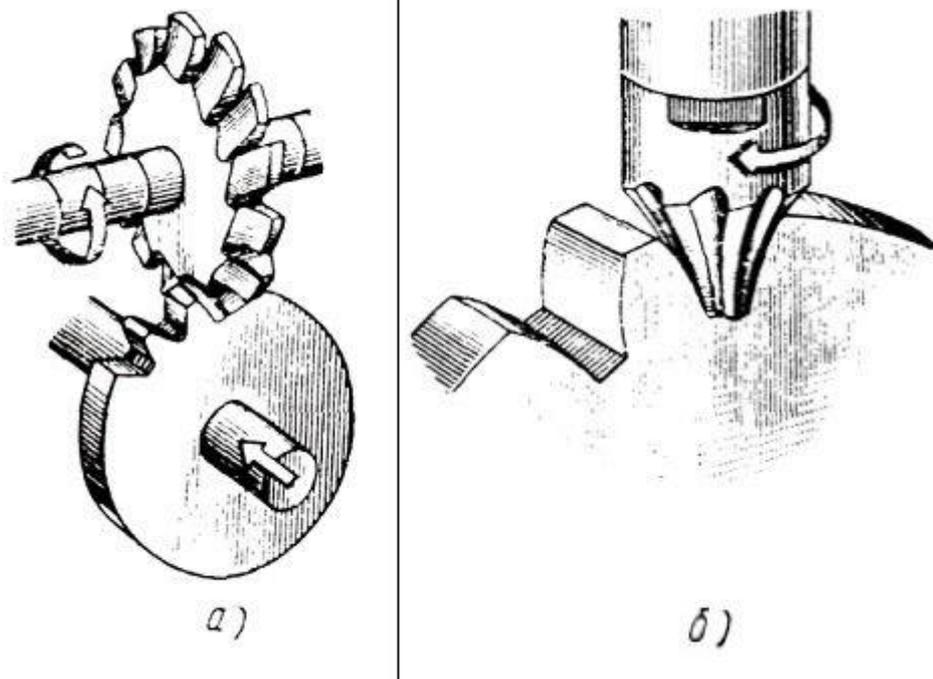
Схема нарезания зубьев модульными фрезами
